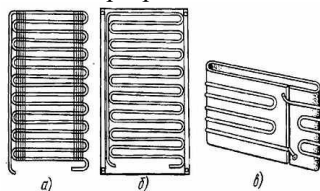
Конструкция конденсаторов холодильного агрегата: а — с проволочным оребрением; б — листотрубчатый; в — прокатно-сварной
